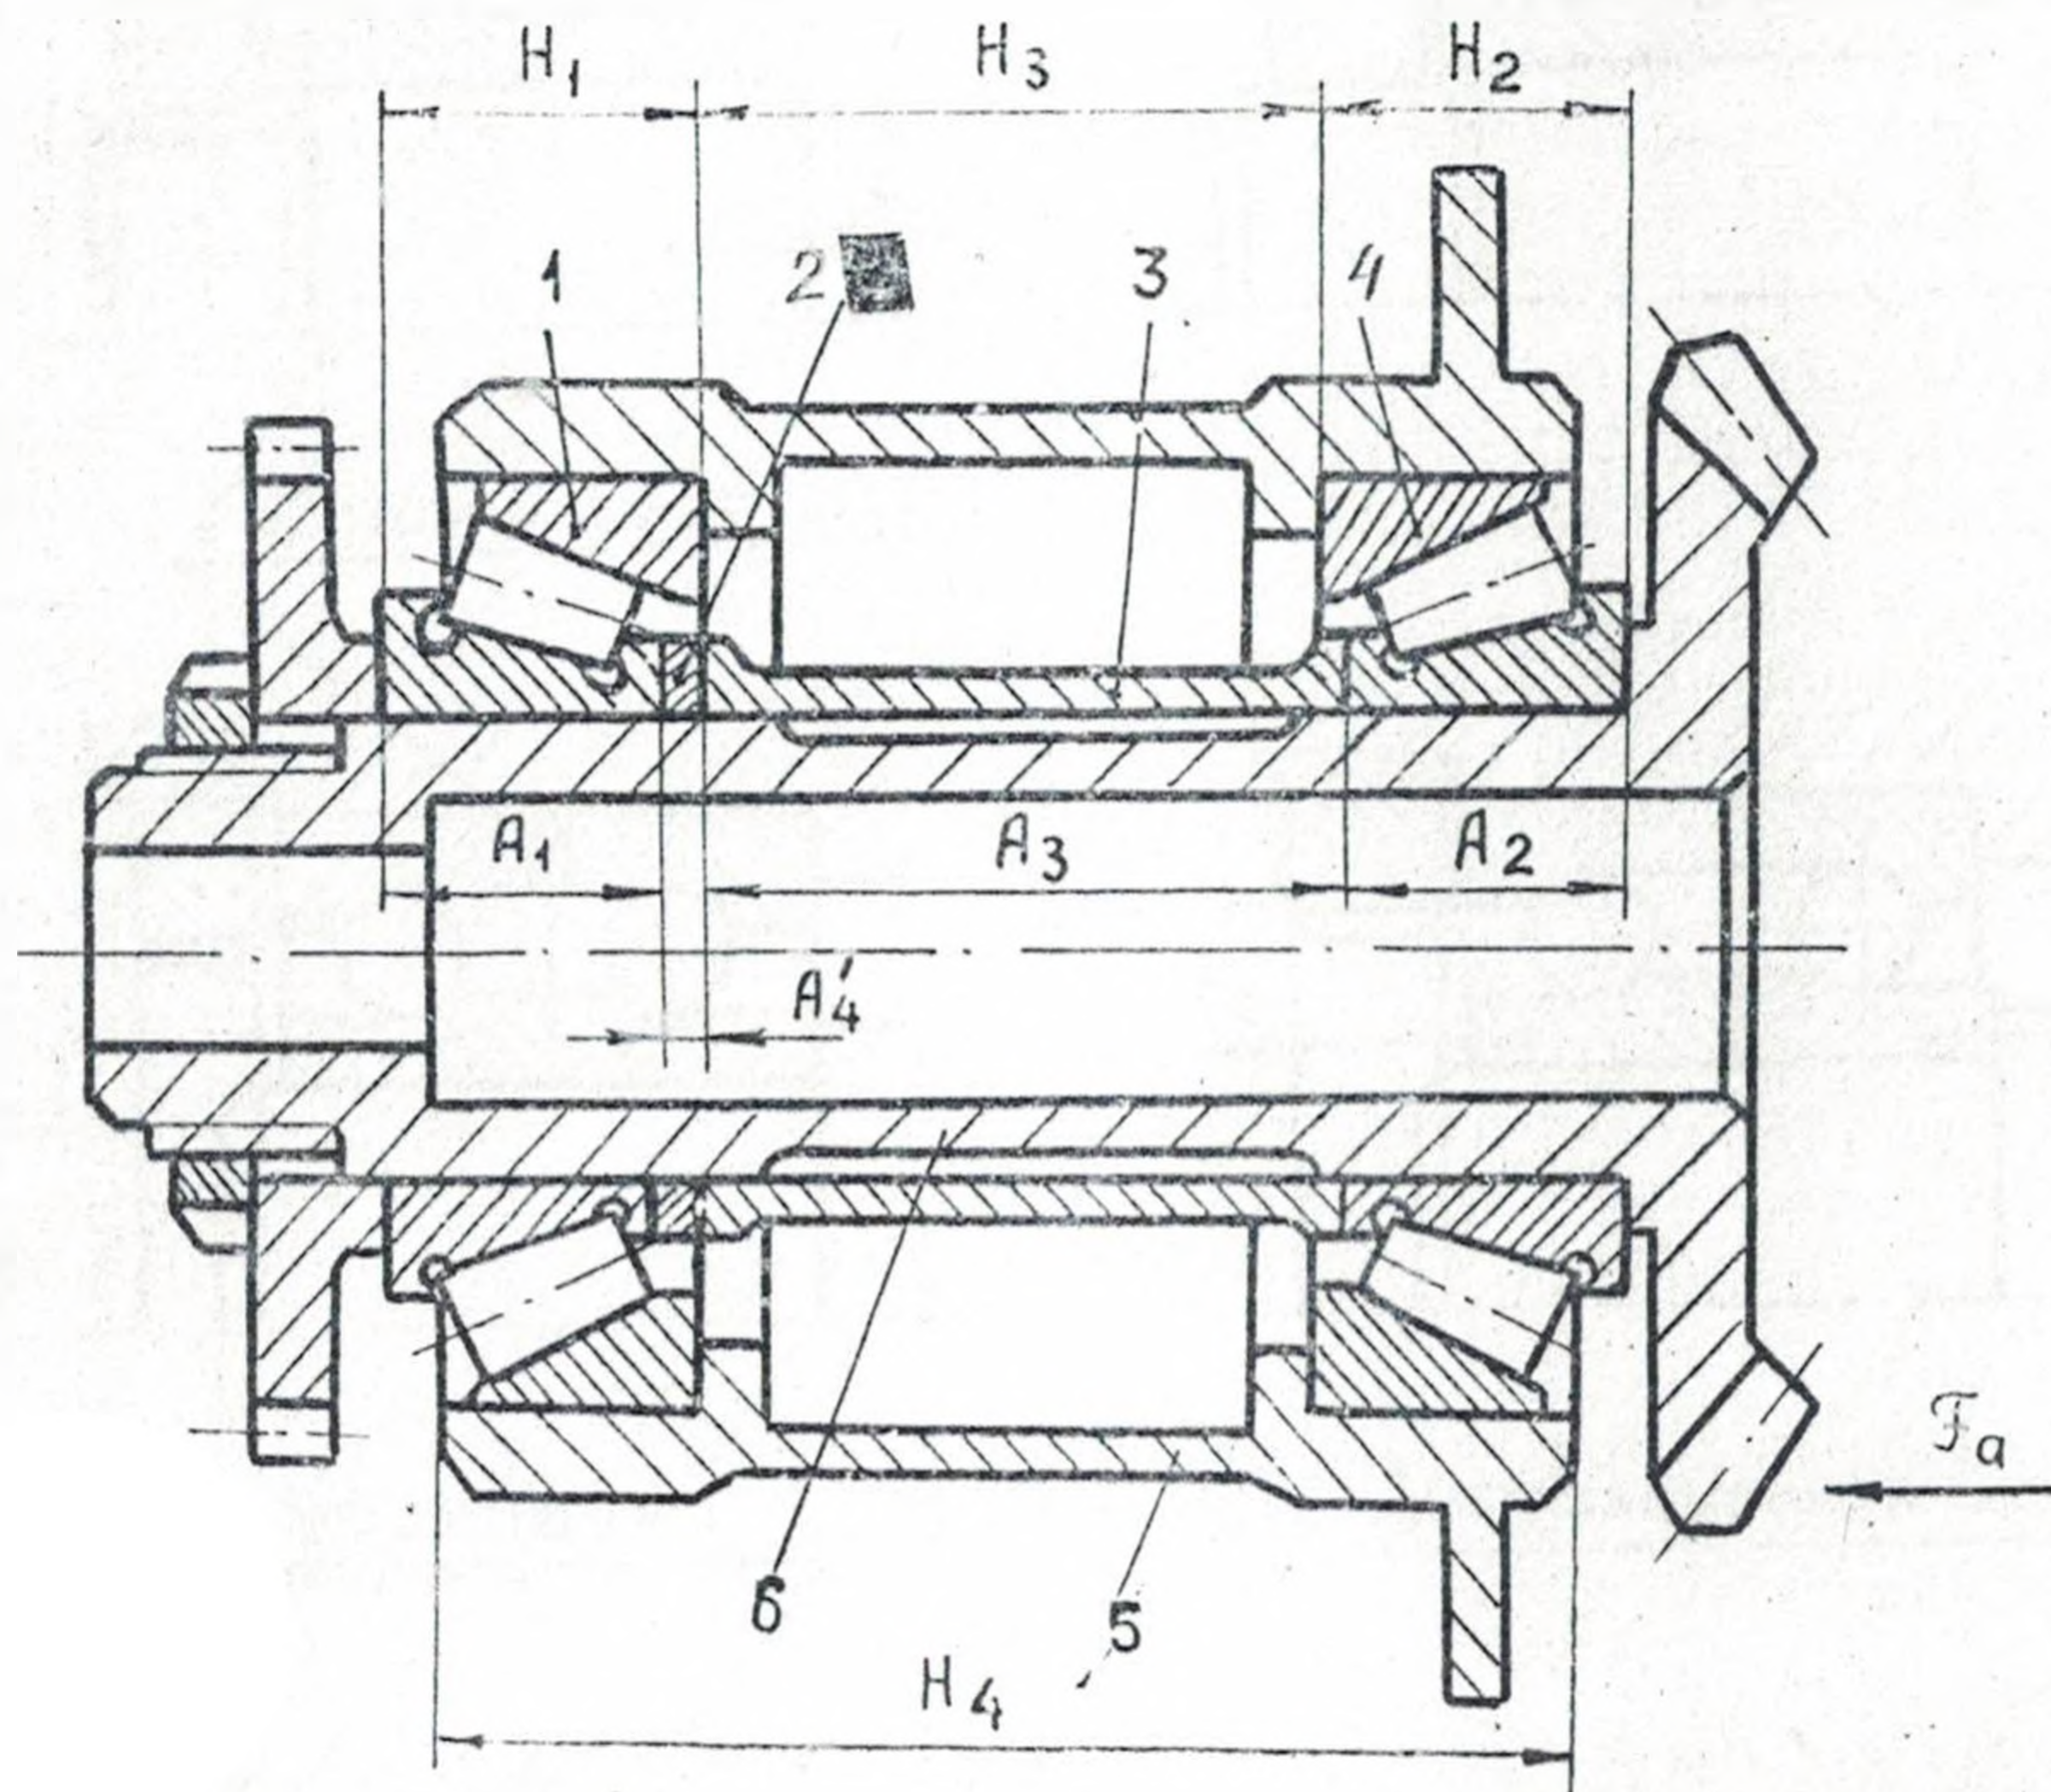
Подшипниковый узел редуктора: 1, 4 — роликовые подшипники; 2 — регулировочное кольцо; 3 — дистанционная втулка; 5 — корпус; 6 — вал-шестерня
